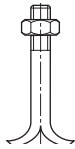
Нівелірні гвинти на поверхні фундаменту
